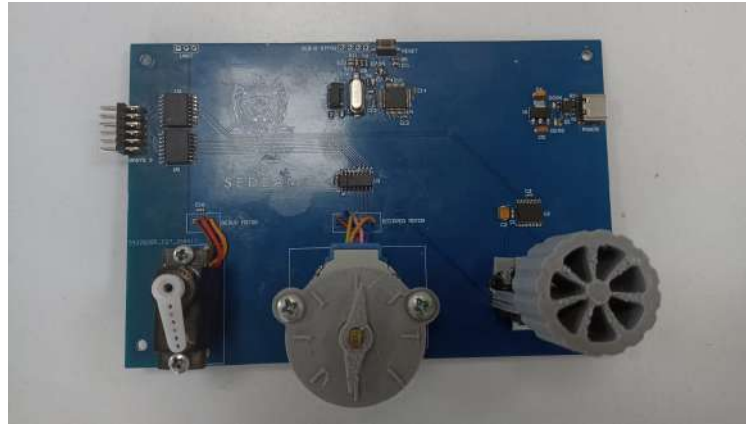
PCB ensamblada con motores y protegida por carcasa impresa.
